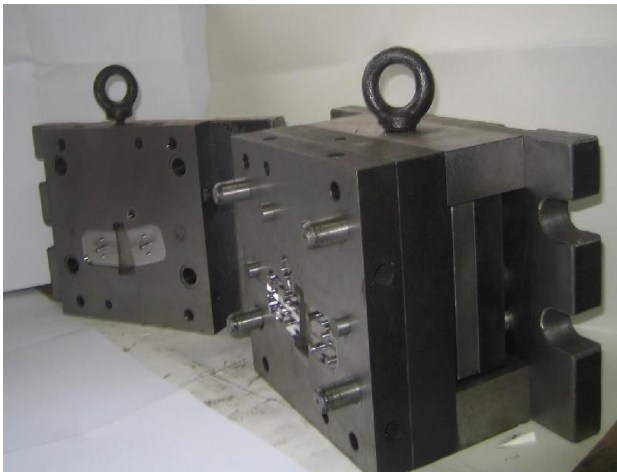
Готова пресформа для виготовлення пресованих деталей.
